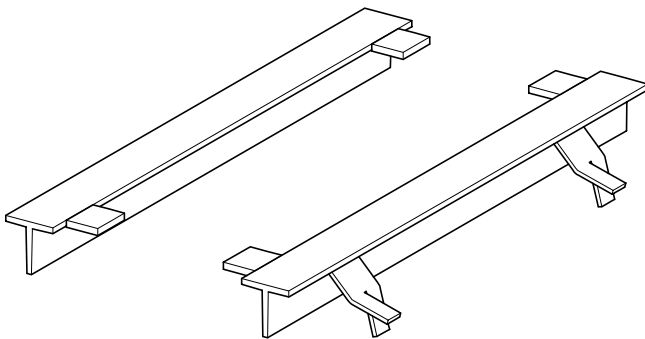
1 Conjunto de barras de apoio (2 peças)
